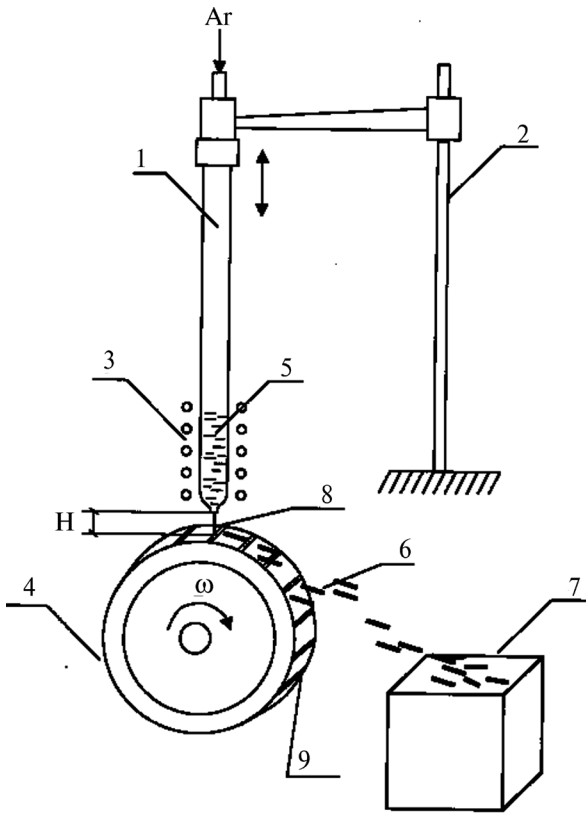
Технологическая схема получения фибры: 1 – кварцевая колба; 2 – механизм перемещения колбы; 3 – индуктор; 4 – закалочный медный диск; 5 – жидкий металл; 6 – фибра; 7 – приемный контейнер; 8 – сопло; 9 – пазы
